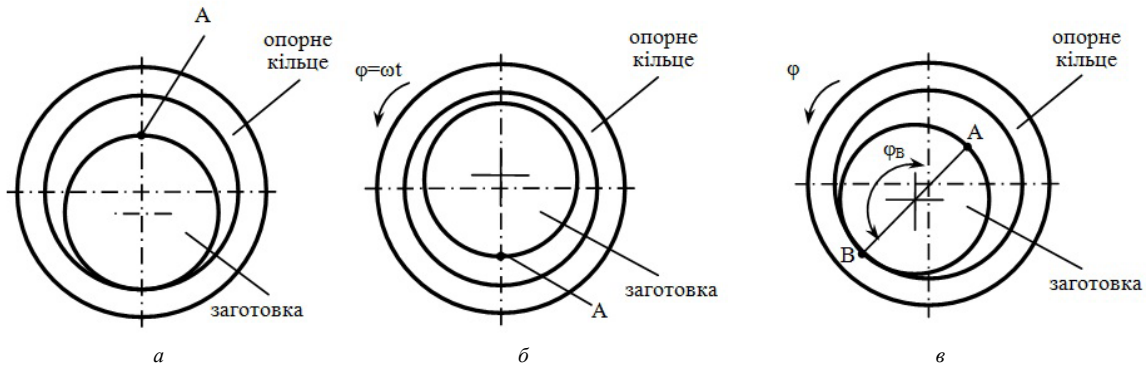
Взаємодія кінцевої частини заготовки з опорним кільцем, встановленим на шпинделі: а – опирання заготовки при її затиску; б – положення кінцевої частини заготовки при повороті шпинделя на кут 180° ; в – положення заготовки в момент повторного контакту з кільцем (поворот шпинделя на кут $180^\circ + \varphi_B$)
